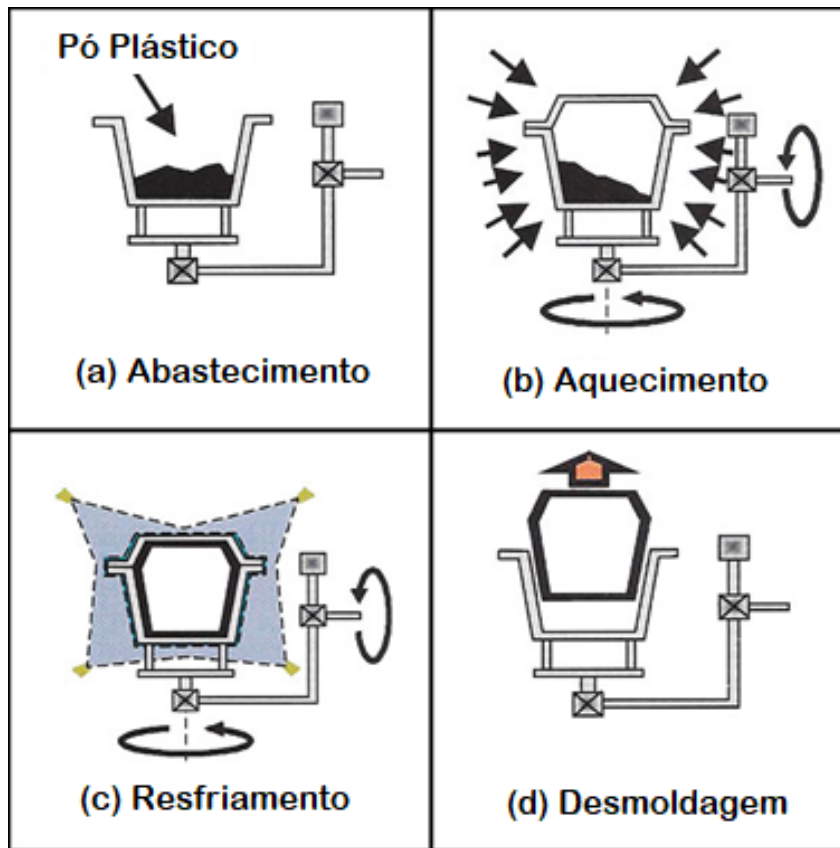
Estágios do processo de rotomoldagem na máquina de rotomoldagem.
